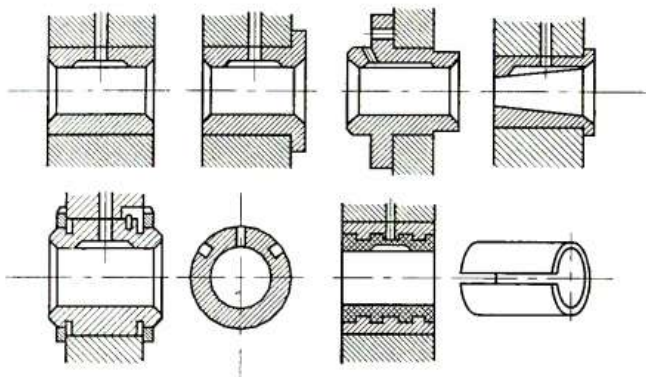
Конструктивні різновиди підшипникових втулок
